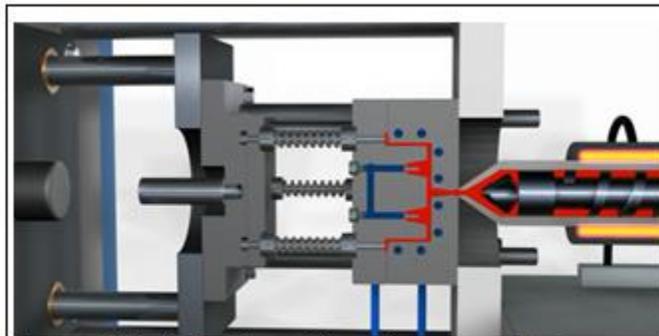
Unidad de inyección y cierre de molde de una maquina inyectora.
